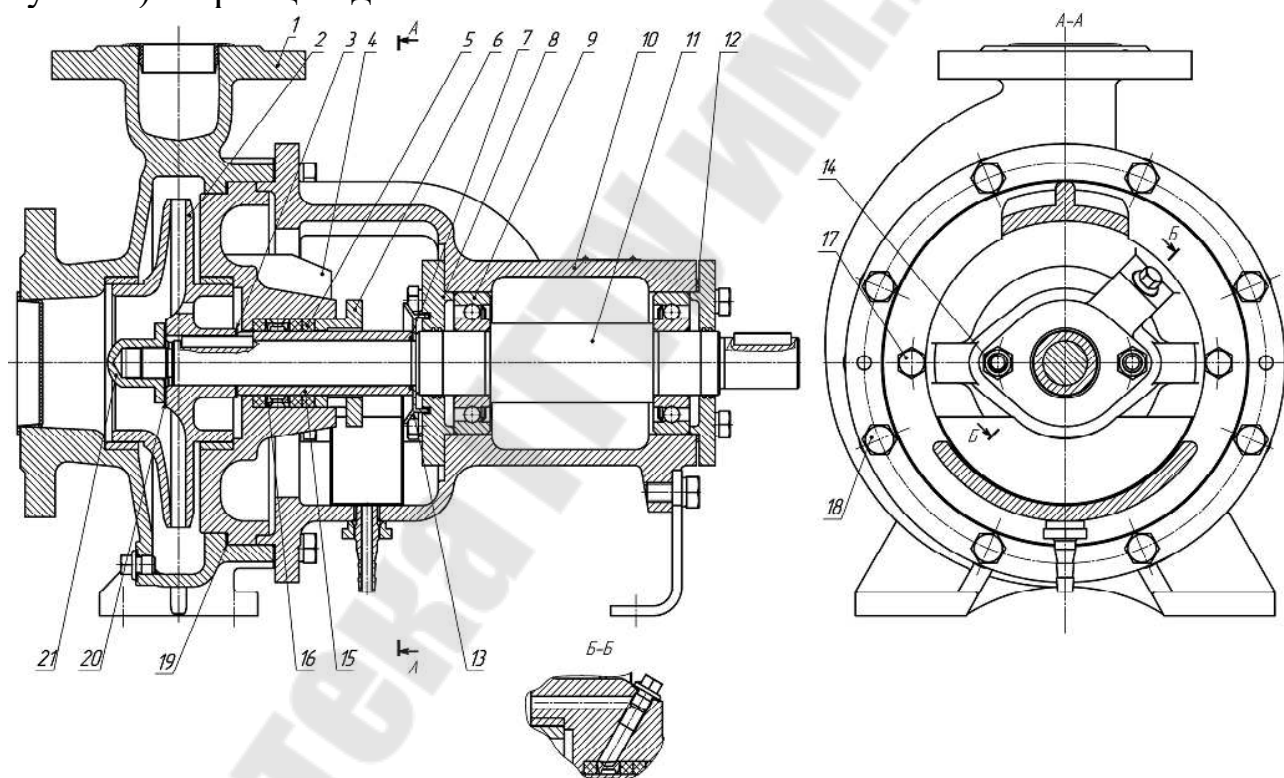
Насос Х-80-50-200-Д: 1 – корпус; 2 - рабочее колесо; 3 – шайба; 4 - корпус уплотнения; 5 – набивка сальника; 6 – сальник; 7 - кольцо резиновое; 8 - крышки подшипников; 9 – радиальные подшипники; 10 – кронштейн; 11 – вал; 12, 19 – прокладки; 13 - отбойное кольцо; 14 – гайки; 15 - втулка защитная; 16 - кольцо сальника; 17, 18 – болты; 20 – неподвижная часть торцевого уплотнения; 21 - обтекатель
